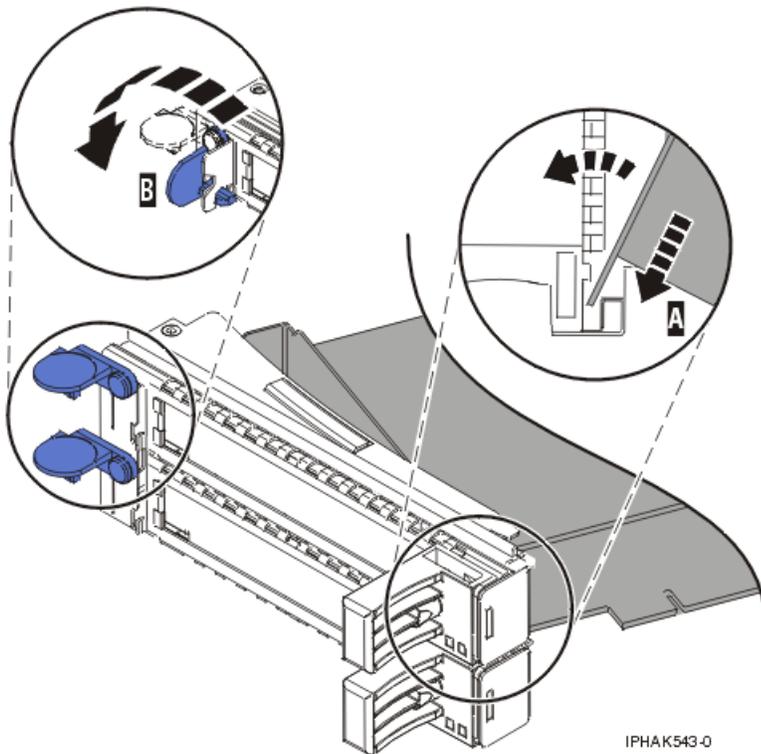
Adaptador que se ha vuelto a colocar en la casete de adaptador PCI
